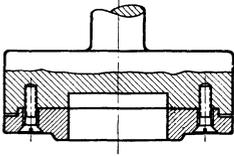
Befestigung der Schnittplatte am „Stempelpkopf“.
